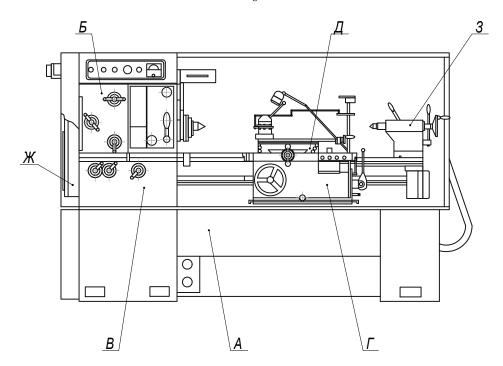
Расположение составных частей станка модели 16Д25
